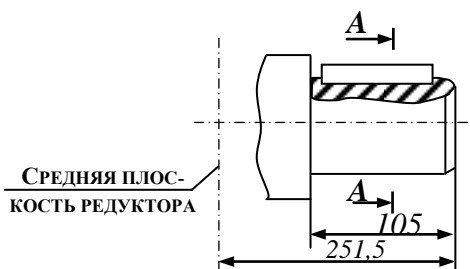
П7 Размеры цилиндрического конца вала редуктора 1Ц2У-200
